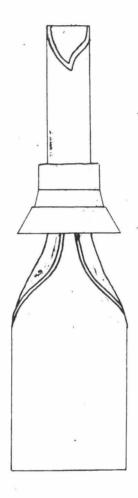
TUBERIA SOLDADA "WELDED BELL".
